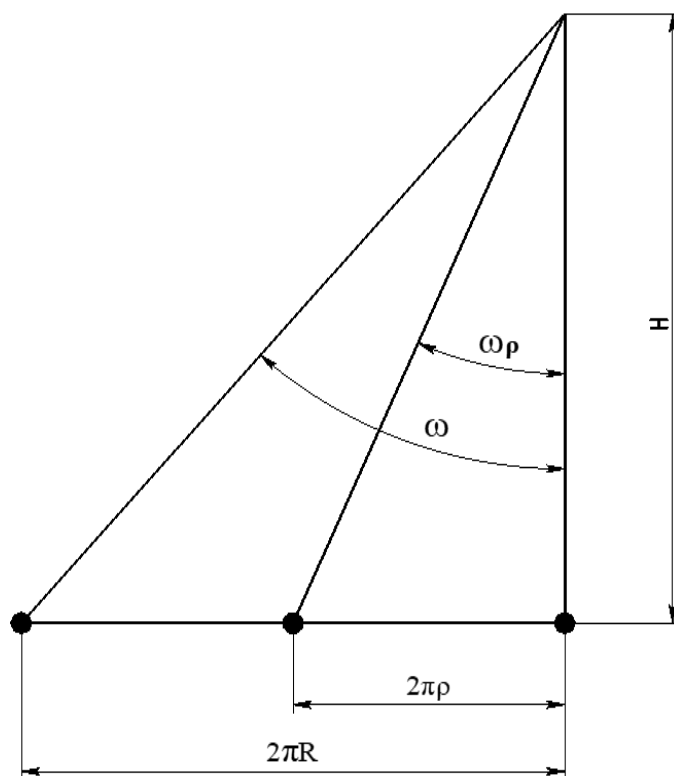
Развёртка винтовых линий канавки сверла на плоскости
